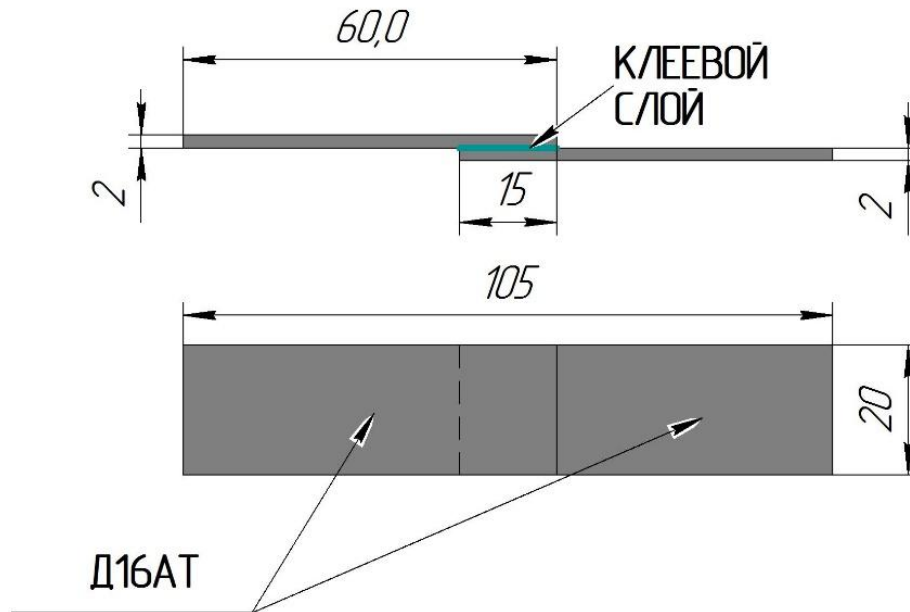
Схема образца для испытания клеевого соединения элементов из сплава Д16АТ, по ГОСТ 14756-69
